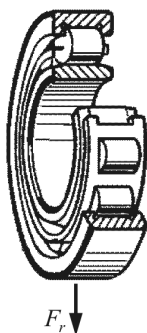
Роликовый радиальный подшипник с короткими цилиндрическими роликами
